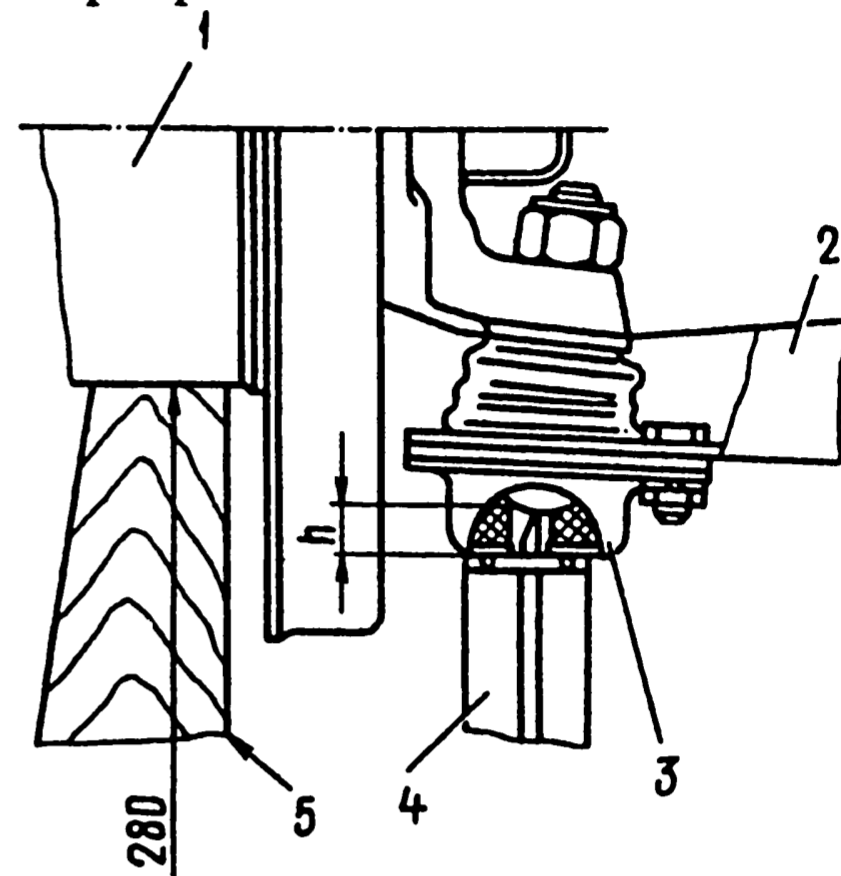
Схема проверки нижних шаровых шарниров: 1 - ступица колеса; 2 - нижний рычаг; 3 - нижний шаровой шарнир; 4 - штангенциркуль; 5 - деревянная колодка
